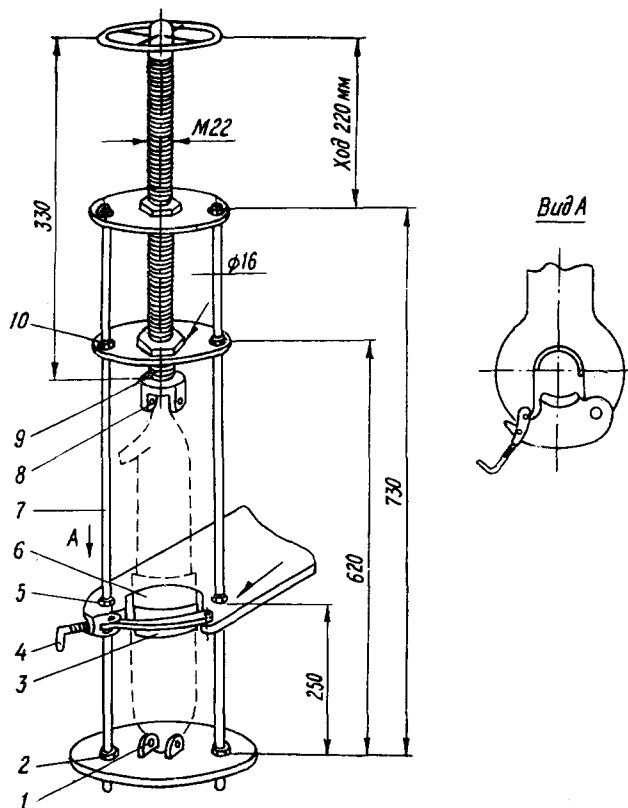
Приспособление для разборки-сборки амортизатора:
